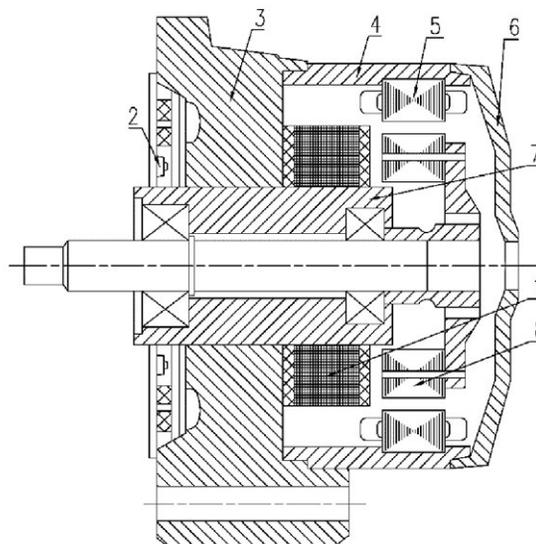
Схематический разрез генератора Niehoff: 1 — обмотка возбуждения, 2 — диоды выпрямителя, 3 — передняя крышка, 4 — корпус, 5 — пакет статора с обмоткой, 6 — задняя крышка, 7 — втулка, 8 — ротор.
